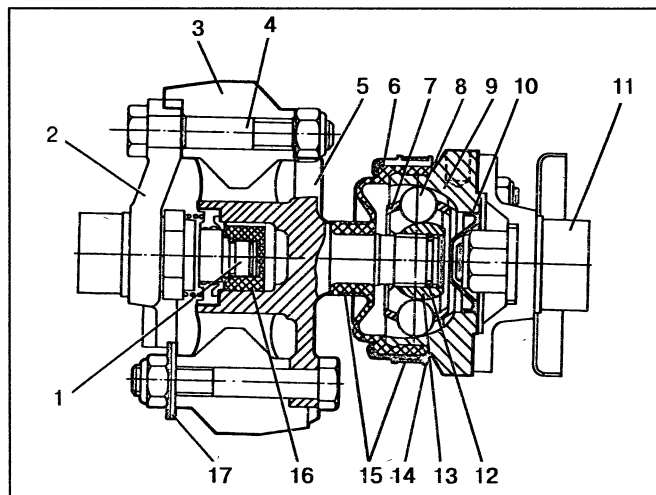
Промежуточный карданный вал: 1 – вторичный вал коробки передач; 2 – фланец вторичного вала; 3 – вкладыш эластичной муфты; 4 – болт крепления фланца; 5 – фланец эластичной муфты; 6 – защитный чехол; 7 – сепаратор; 8 – шарик; 9 – корпус шарнира равных угловых скоростей; 10 – заглушка; 11 – ведущий вал раздаточной коробки; 12 – стопорное кольцо; 13 – обойма шарнира; 14 – защитный колышек чехла; 15 – хомуты; 16 – центрирующая втулка; 17 – балансирующая шайба
